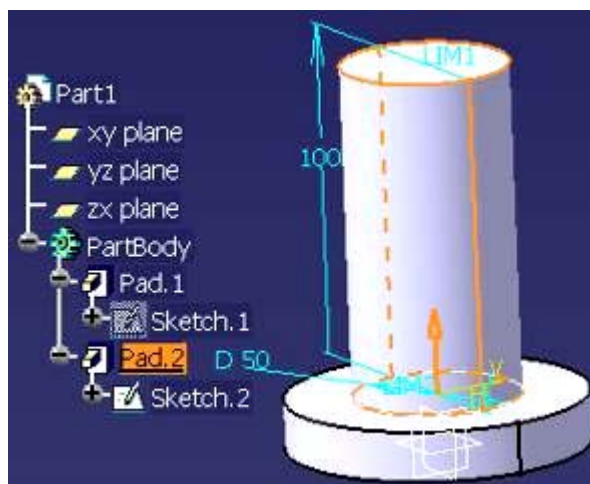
Obținerea celui de-al doilea cilindru din corpul robinetului
